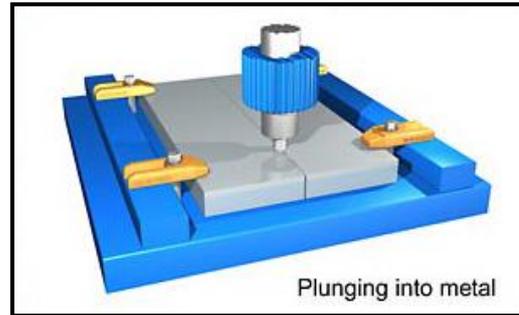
Proses *Friction Stir Welding* (Reynolds, 1997)
